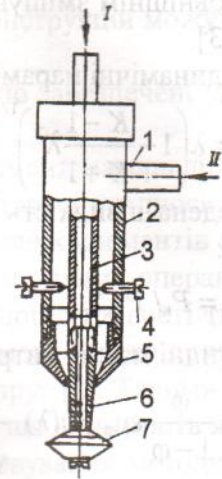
Схема пневматичної форсунки для розпилювання рідин:
